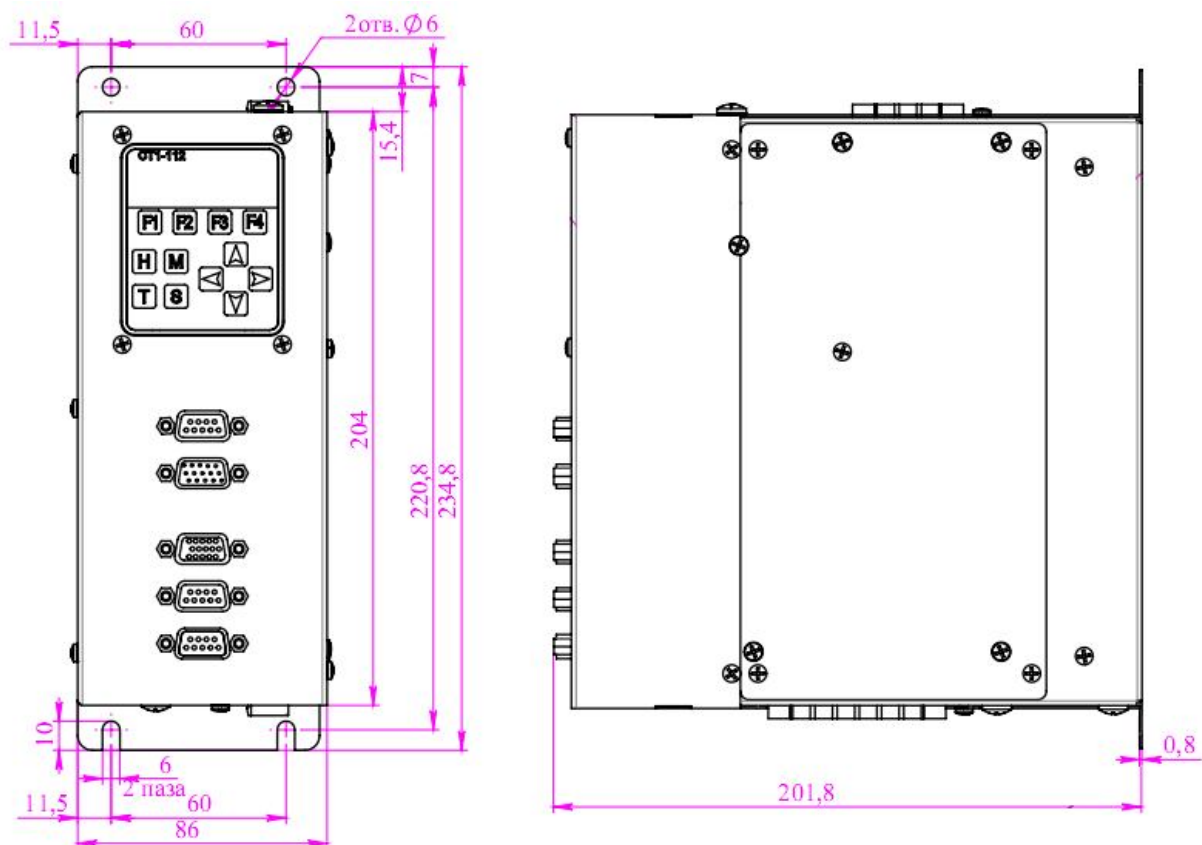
Габаритные и присоединительные размеры сервоусилителя СПС25-xx.
